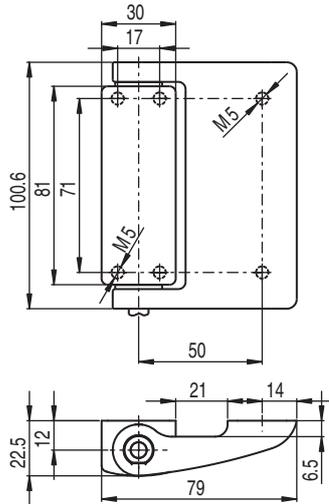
Dimensões do S410-M1CB2-B em mm
